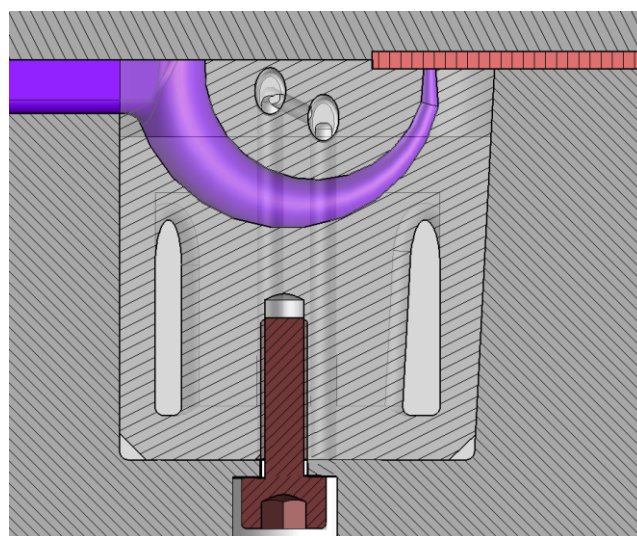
Exemplo de montagem do inserto de injeção MTO.
